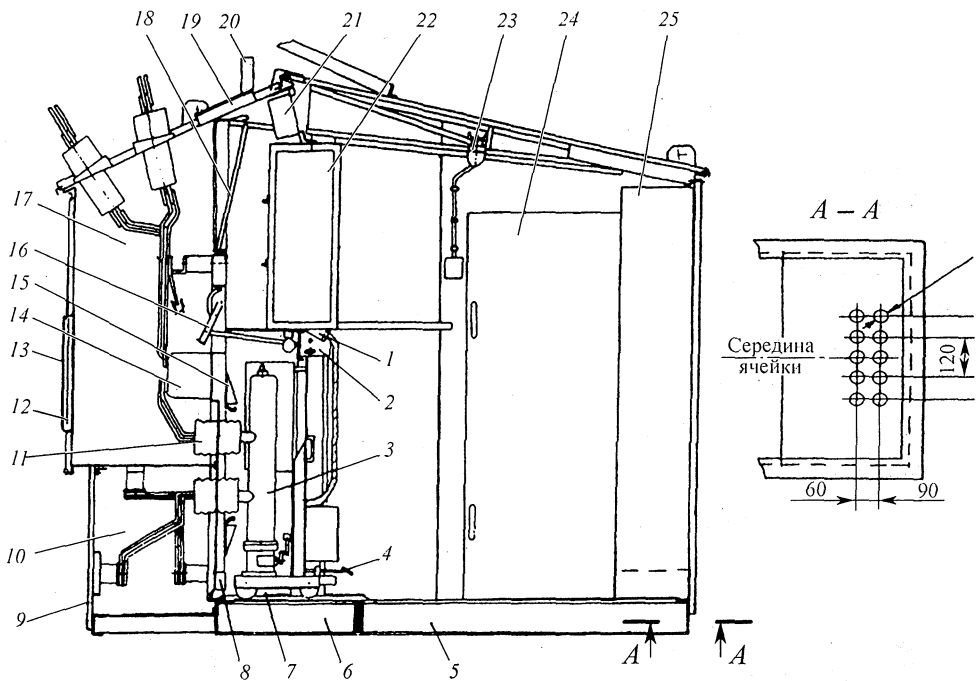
Разрез КРУН на ток 1600 А с воздушным вводом по ячейке: 1 — штепсельный разъем; 2 — привод заземляющего разъединителя; 3 — тележка с высоковольтным выключателем; 4 — педаль фиксатора положения ячейки; 5 и 6 — рамы основания блока; 7 — отсек тележки; 8 — электронагреватель; 9 — съемная стенка; 10 — отсек сборных шин; 11 — изолятор проходной с неподвижными разъединяющими контактами; 12 — предохранительная перегородка; 13 — дверь отсека ввода; 14 — трансформатор тока; 15 — защитные шторки; 16 — заземляющий разъединитель; 17 — отсек ввода; 18 — дифференциальный клапан; 19 — разгрузочный клапан; 20 — кронштейн ввода; 21 — вентиляционная перегородка; 22 — релейный шкаф; 23 — узел освещения; 24 — коридор управления; 25 — блок релейных шкафов
